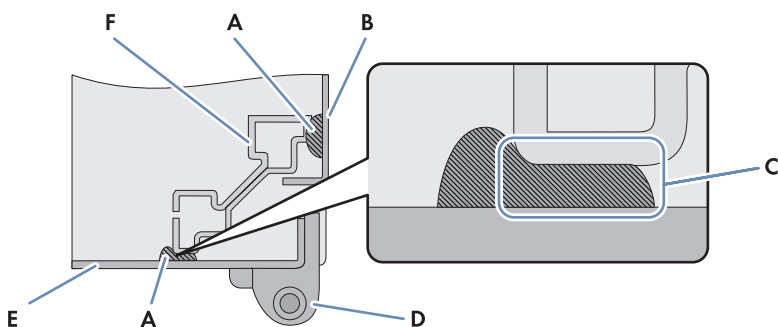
Sezione della vista in pianta delle guarnizioni (esempio)
